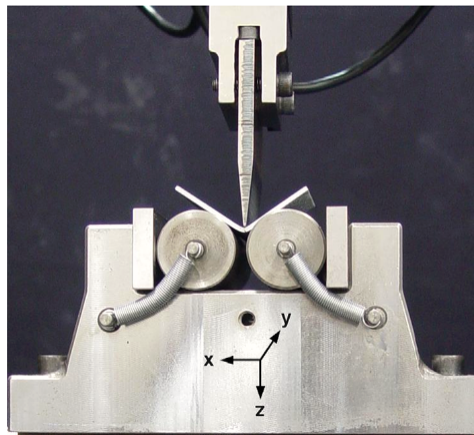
Machine de flexion pour un essai macroscopique sur une tôle d'acier [Mishra and Thuillier, 2014]
